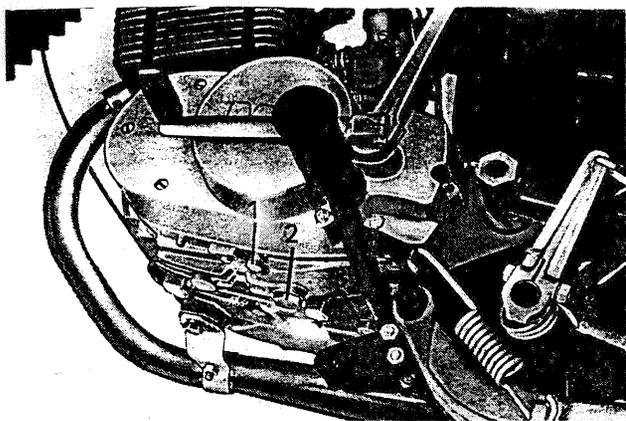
Vidanger le lubrifiant de la chambre d'engrenages et d'embrayage
